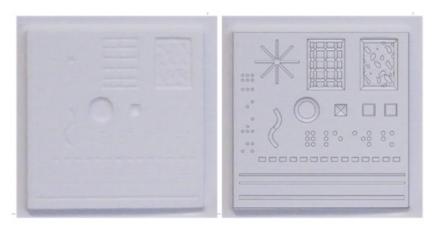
Imagen del termoconformado sobre molde en positivo (izquierda), y su superposición fotográfica con la geometría teórica diseñada (derecha)
